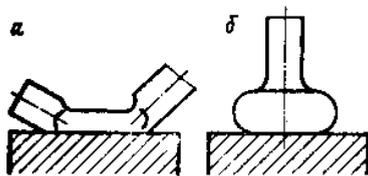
Виды термокомпрессионной сварки по способу выполнения соединения:
